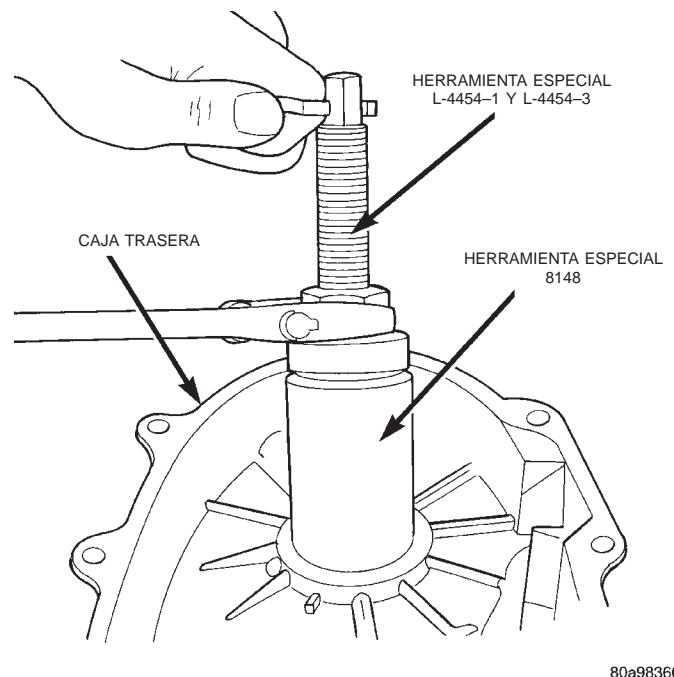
Desmontaje del cojinete trasero del eje transmisor
